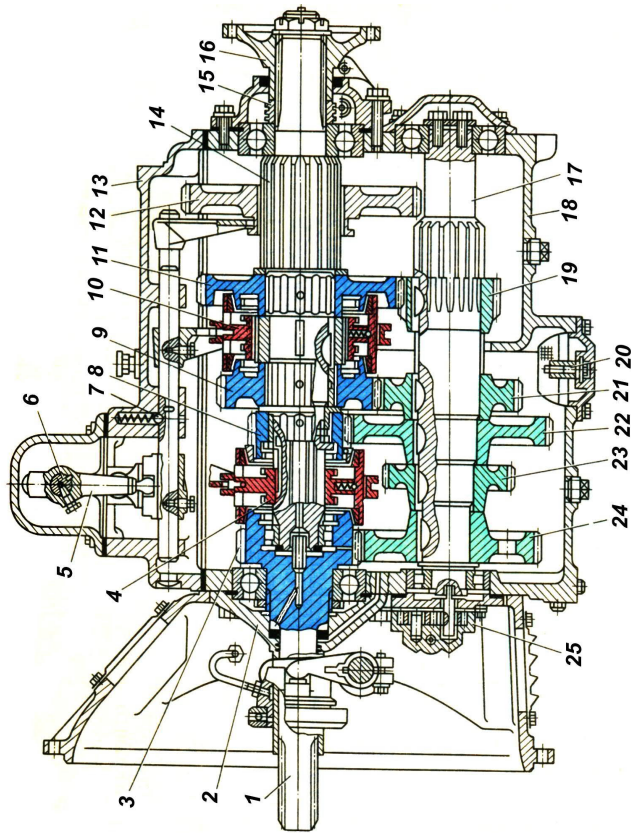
Устройство коробки передач автомобиля МАЗ-5335:
